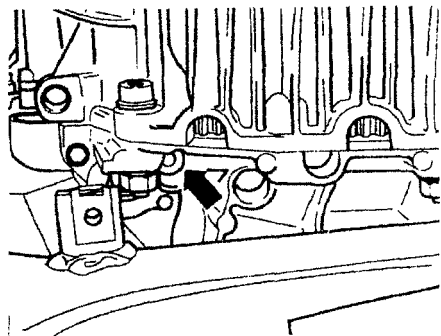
Местоположение пробки удаления охлаждающей жидкости из блока цилиндров шестицилиндрового двигателя
